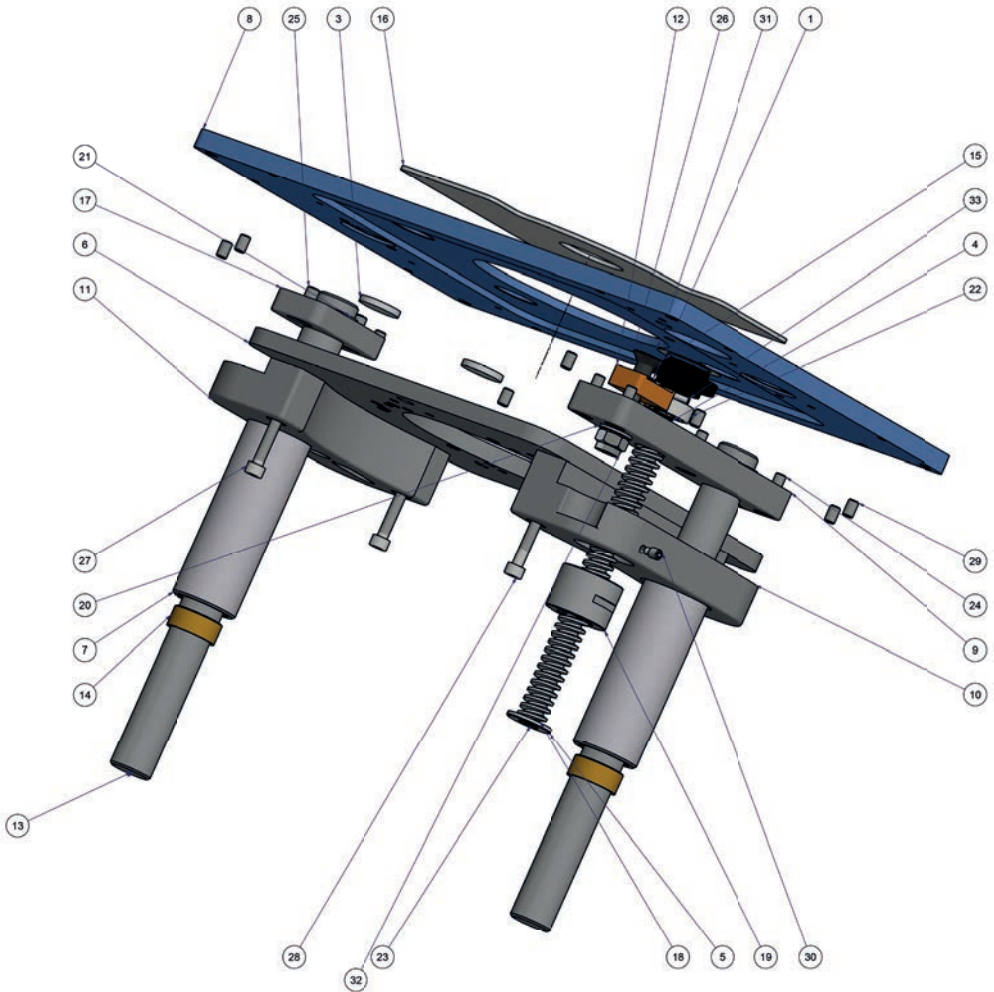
Explosionszeichnung OFL2.0 und OFL2.0-MINI
